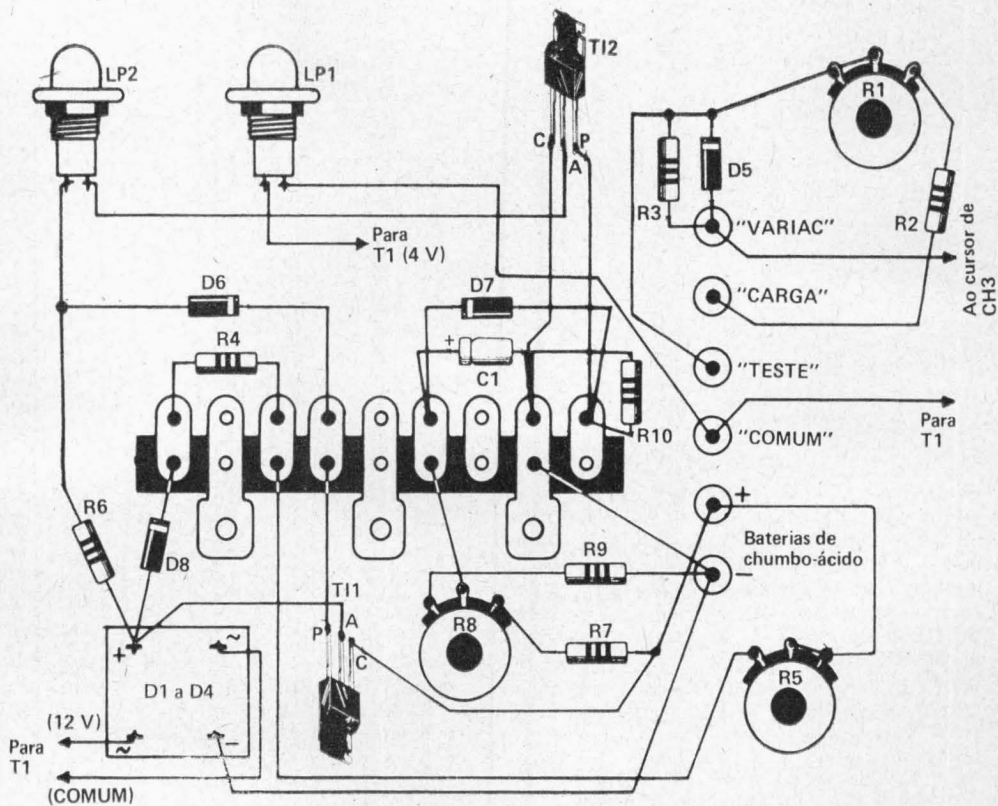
Chapeado do circuito da Fig. 1. O Autor optou pela montagem tipo ponto-a-ponto, utilizando pontes de terminais. Deste desenho só falta o transformador T1, chave CH1 e fusível F1.
